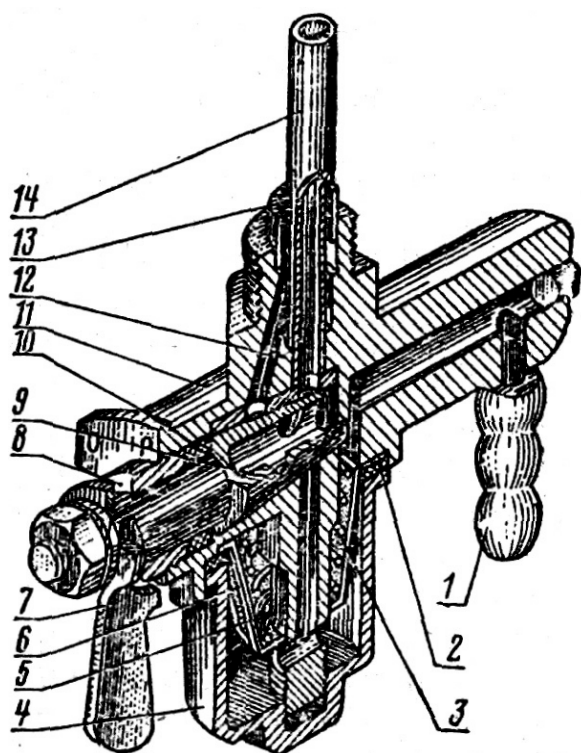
Бензокраник КР-12: 1 — штуцер; 2 — прокладка; 3 — сетка фильтра; 4 — стакан отстойника; 5 — пружина фильтра; 6 — каркас фильтра; 7 — рукоятка; 8 — гайка сальника; 9 — золотник; 10 — сальник; 11 — корпус бензокраника; 12 — отверстие резерва; 13 — трубка резерва; 14 — трубка основной подачи топлива
